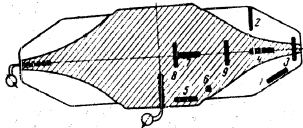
Схема отбора образцов от штампков после ступенчатой и вторичной закалки (цифры указывают номера образцов)
